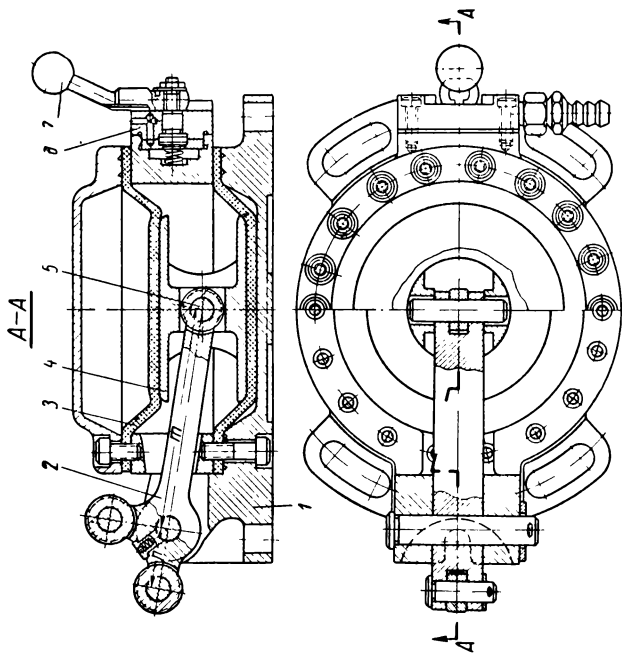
Отделенный диафрагменный пневматический привод с рычагом-усилителем
